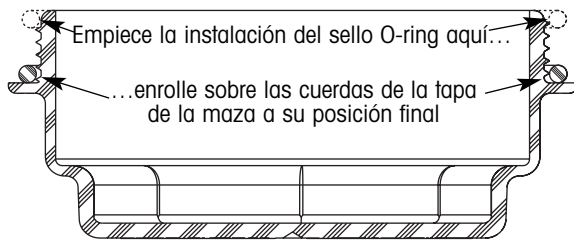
Detalles de instalación del sello O-ring de la tapa de la maza
